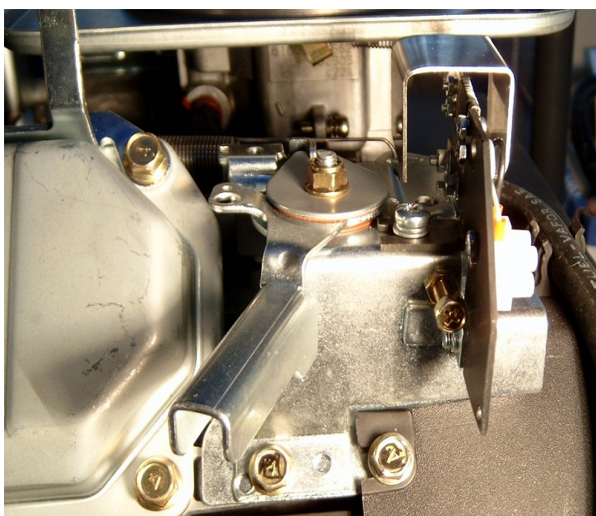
и П2.5. Установленный привод на двухцилиндровых двигателях.
